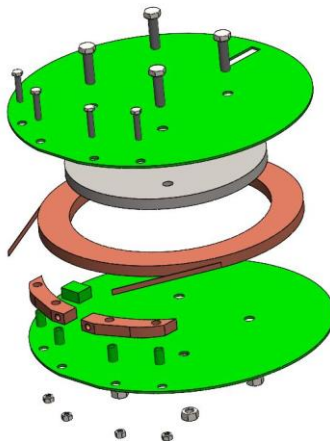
Explosionado de los componentes del CAS. Fuente: Cyclomed.
